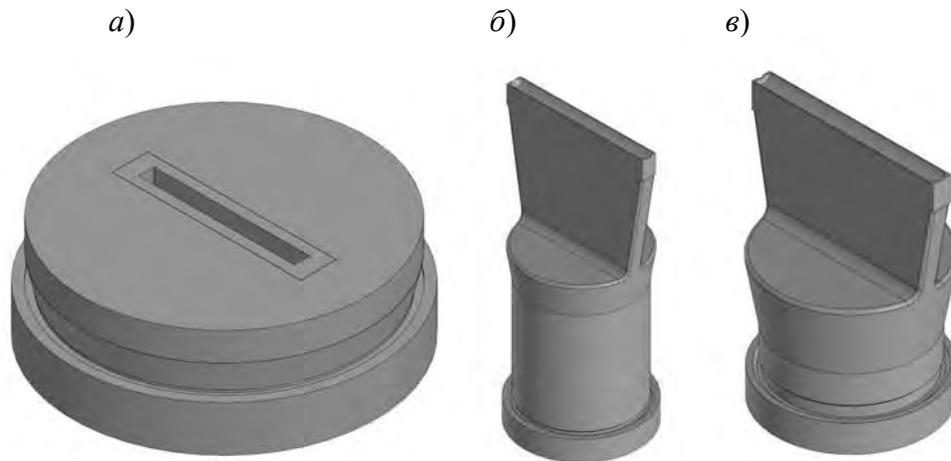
3D-модели оснастки для прессования твердосплавных стержней на сервоприводном прессе: *a* – матрица; *б* – нижний пуансон; *в* – верхний пуансон
